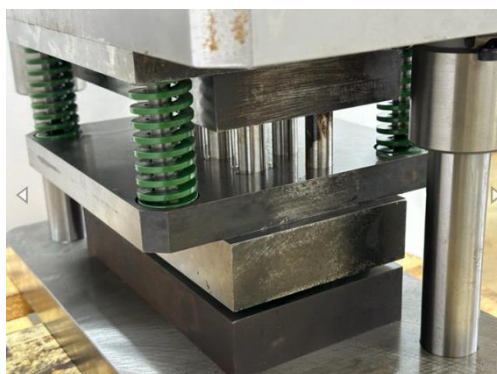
Загальний вигляд багатогніздної прес-форми
